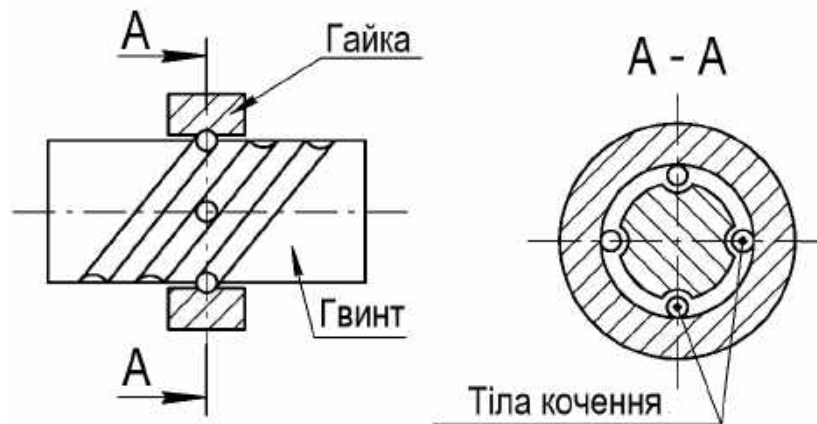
Конструктивна схема кулькопідшипникової передачі
